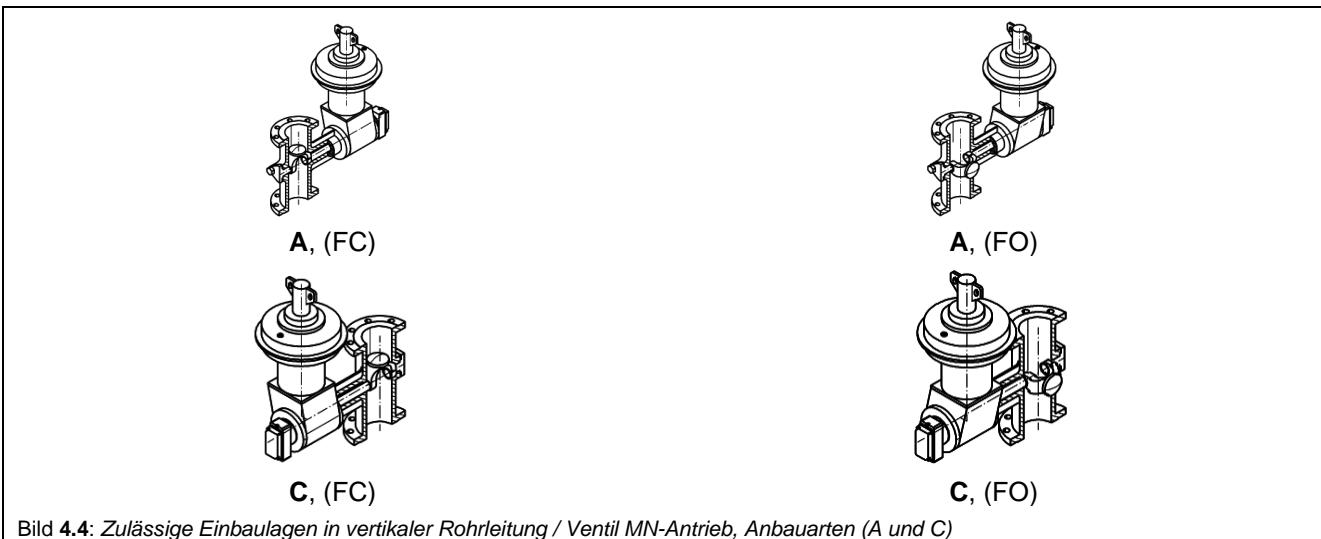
Zulässige Einbaulagen in vertikaler Rohrleitung / Ventil MN-Antrieb, Anbauarten (A und C)
